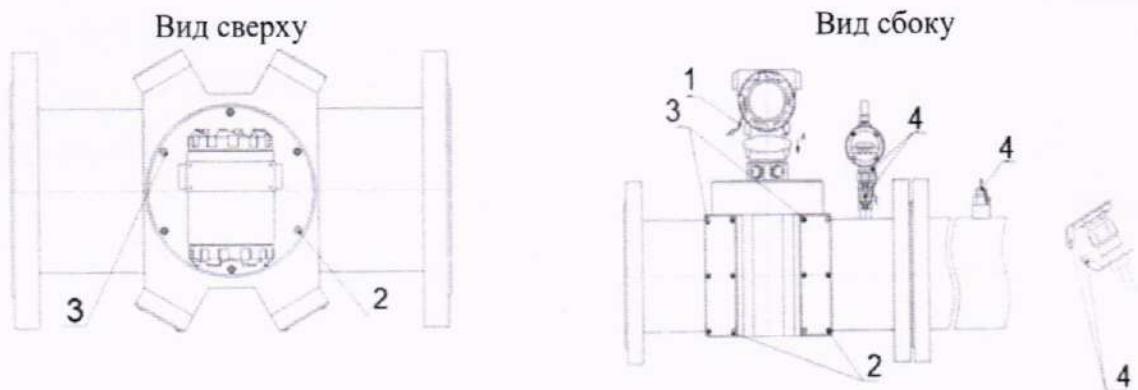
Корпус круглого сечения с раздельными защитными крышками
